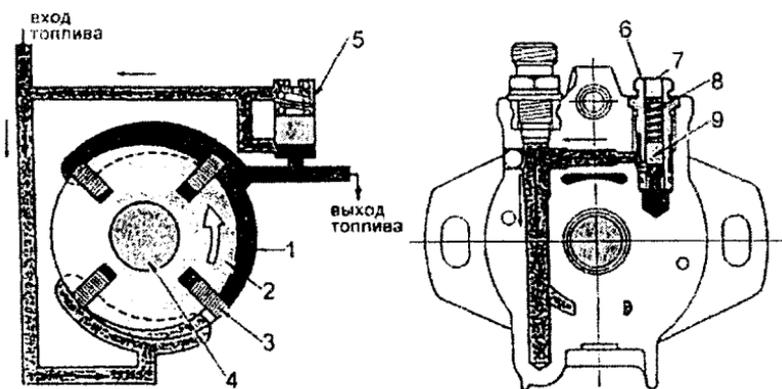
Топливный насос низкого давления и регулирующий клапан:
